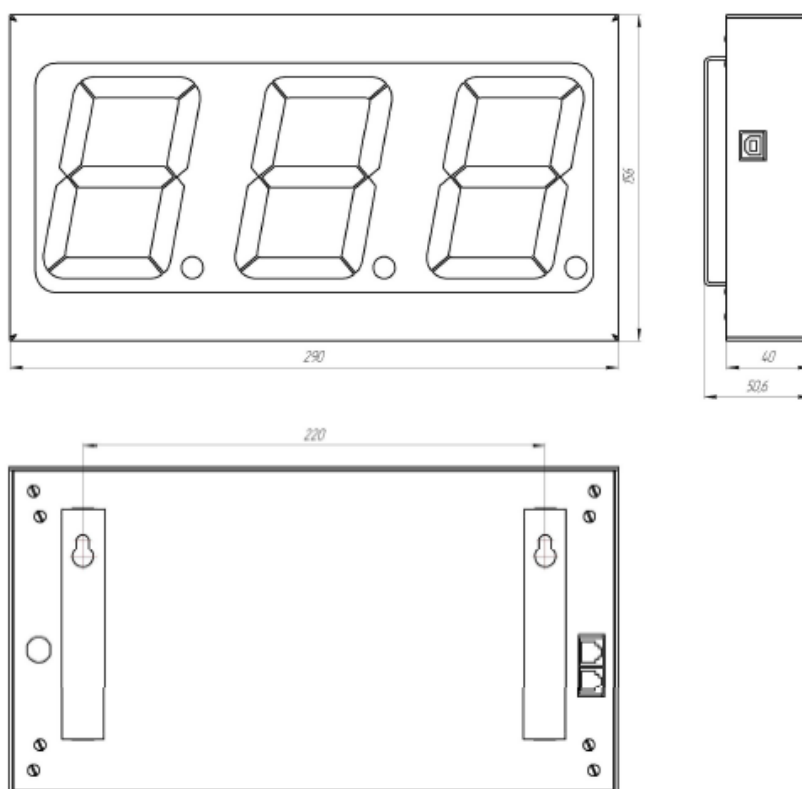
Общий вид, габаритные размеры и элементы конструкции TI-D100x3R- DB9-220: 1 – корпус, 2 – крышка корпуса, 3, 4 – разъемы DB-9 интерфейса RS232/RS485, 5 – разъем сетевой  $\approx 220$  В
